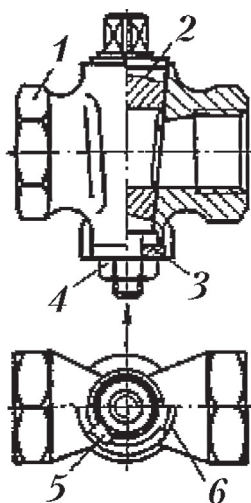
Натяжной муфтовый кран с резьбовой затяжкой:
